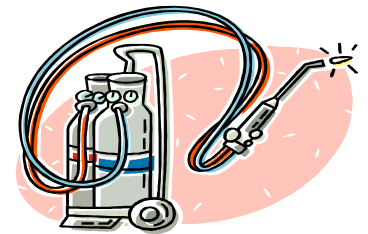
Unidade de soldadura oxiacetileno com retentor de flashback. Fonte: <https://ubisafe.org/image/torch-vector-welding/1432688.html>
